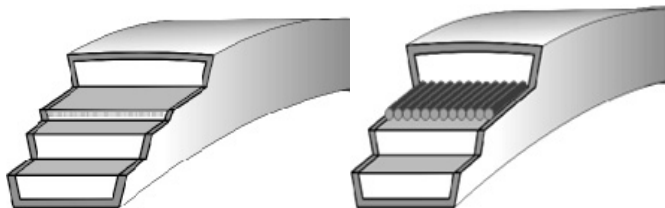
Общий вид клинового ремня кордтканевой и кордшнуровой конструкции
